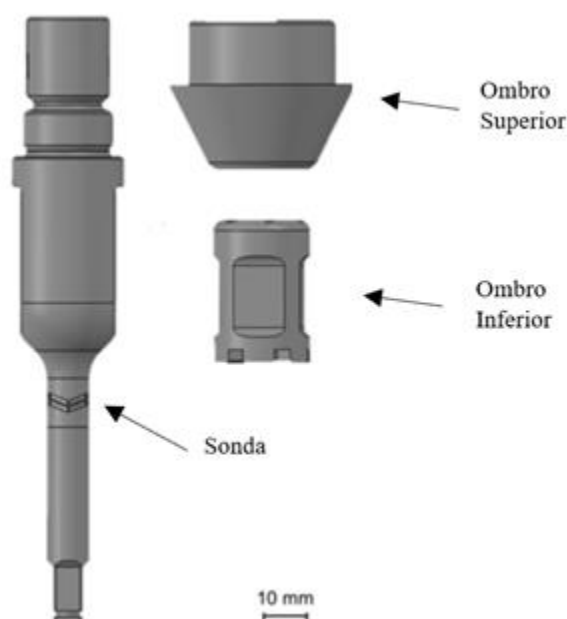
Ferramenta utilizada na soldagem por BT-FSW
